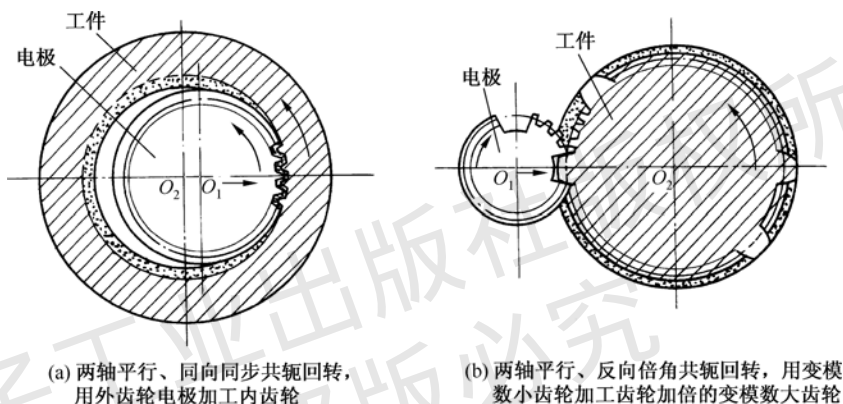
电火花共轭回转加工精密内齿轮和变模数非标齿轮
